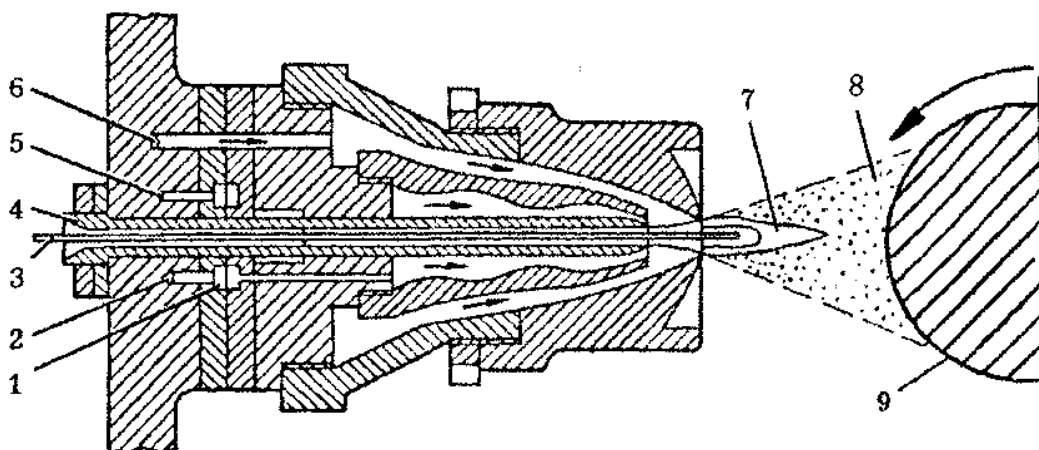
Розпилювальна головка газополуменевого металізатора:
